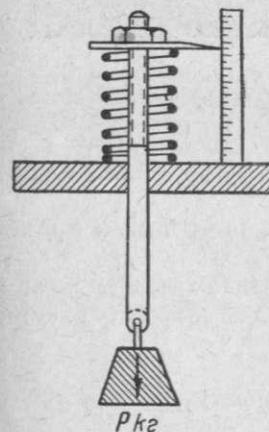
Схема приспособления для замера упругости клапанных пружин.
